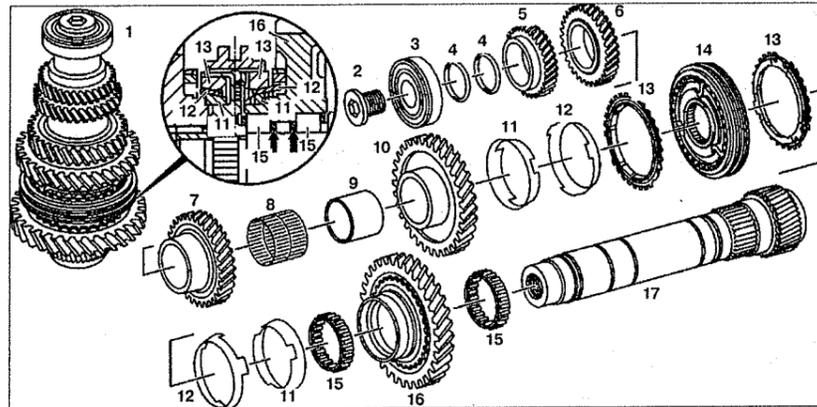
Ведомый вал (автомобили с двигателями 111.948 и 601.970):
